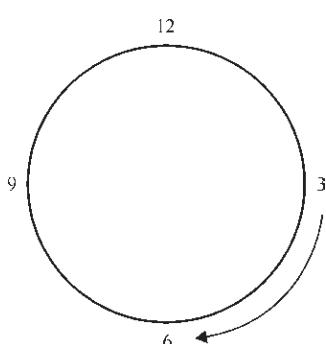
Пространственные положения сварки для неповоротной трубы
